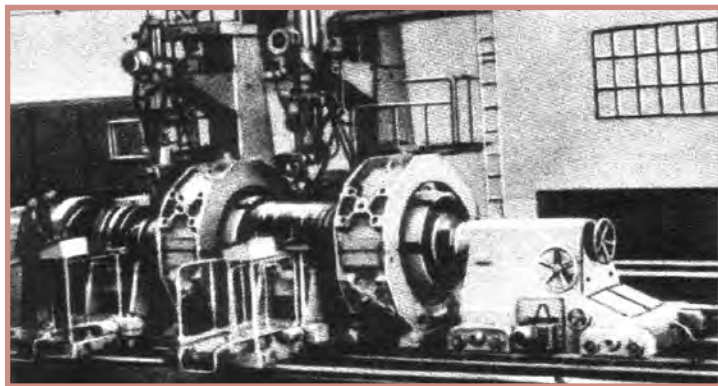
Наплавка вала блюминга на вальценаплавочном станке КЖ–9705
